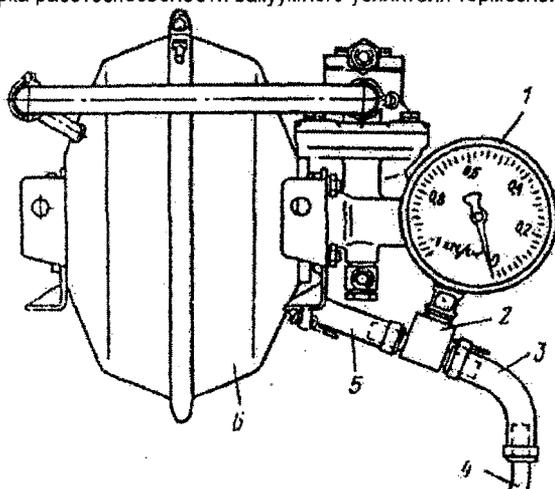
Проверка работы гидровакуумного усилителя с помощью тройника с вакуумметром: 1 – вакуумметр; 2 – тройник; 3 – трубопровод от впускного коллектора двигателя; 6 – корпус диафрагмы усилителя
